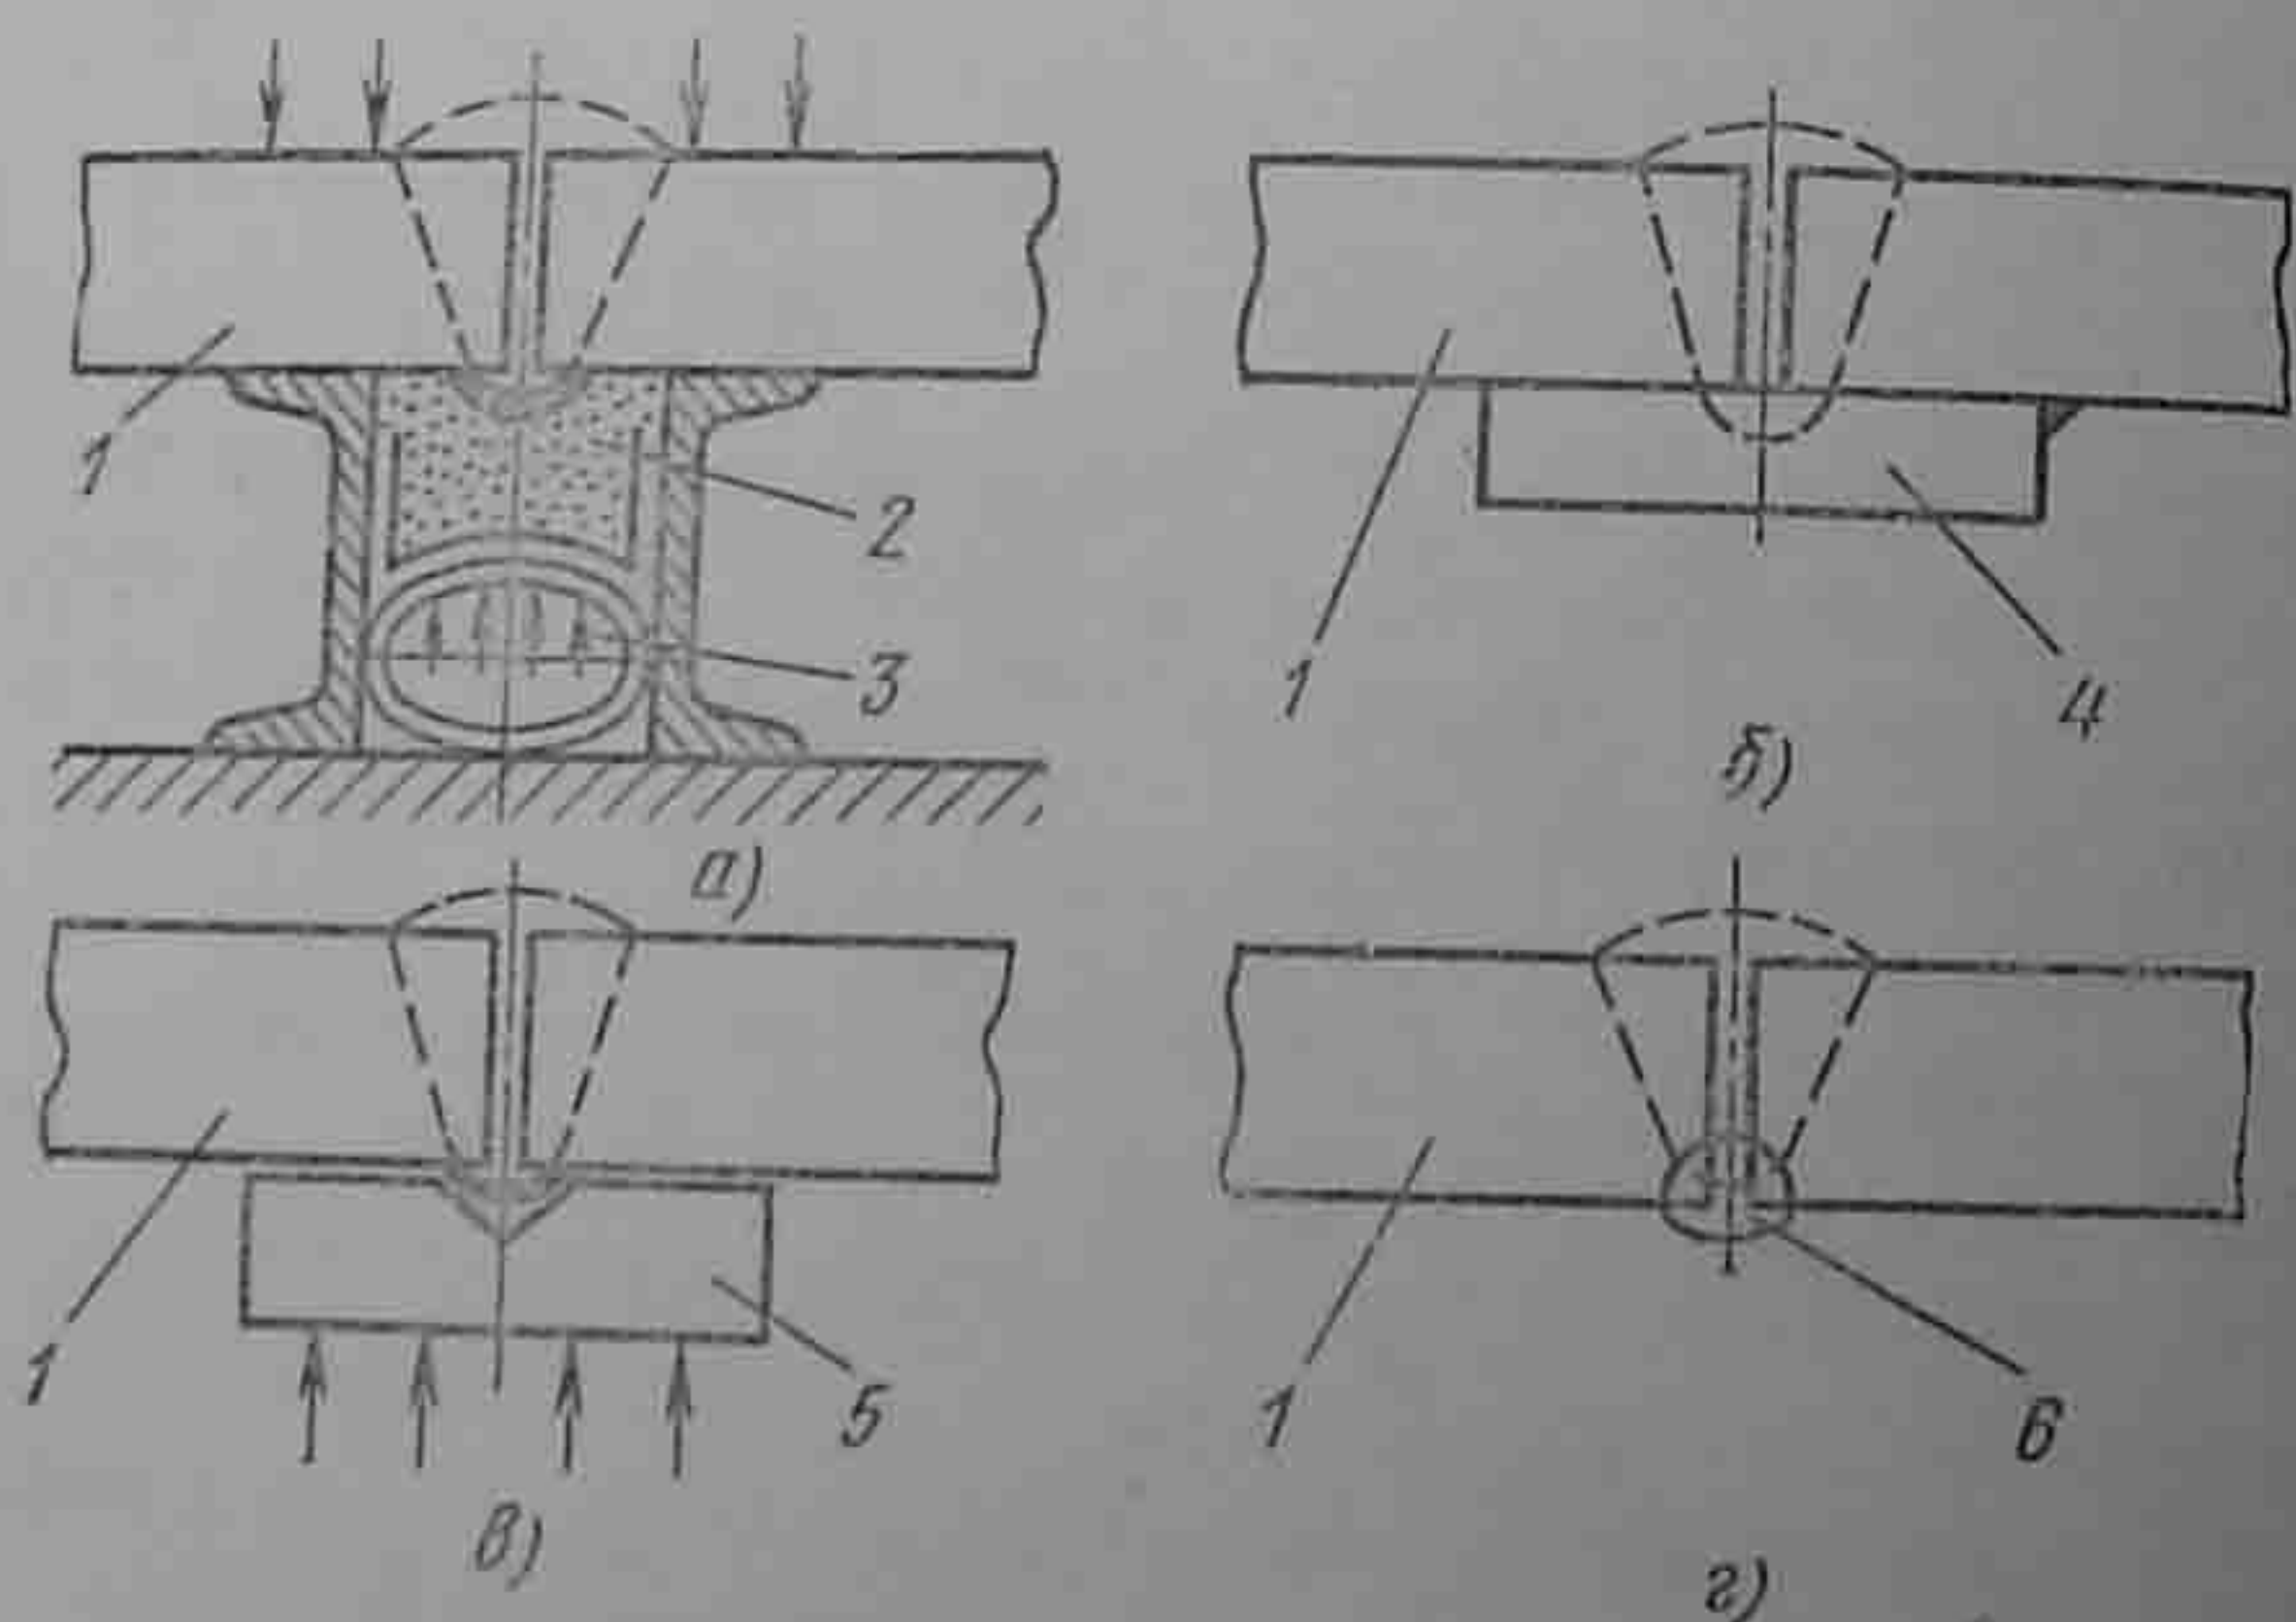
Приспособления для односторонней автоматической сварки:
